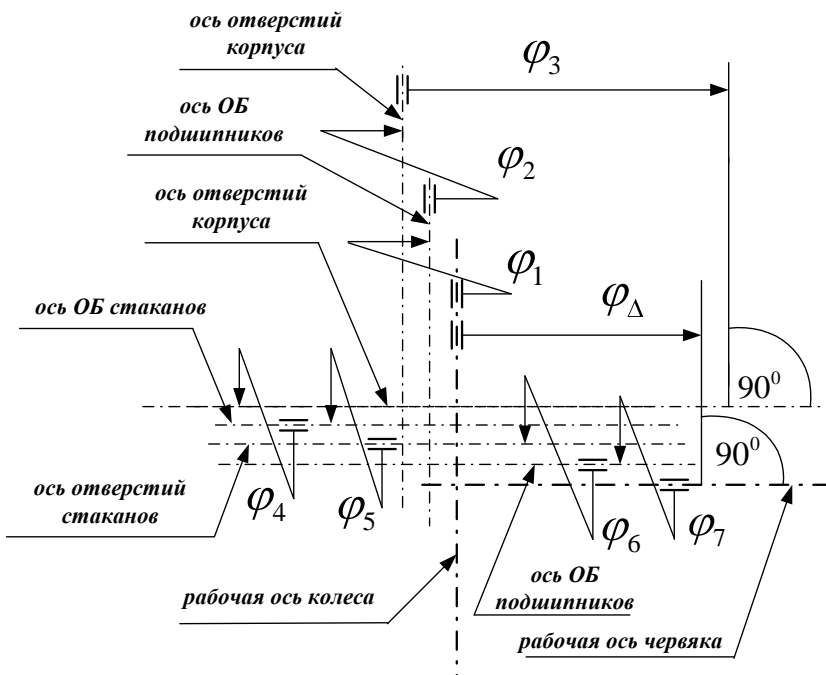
Схема размерной цепи, описывающей формирование межосевого угла червячной передачи
